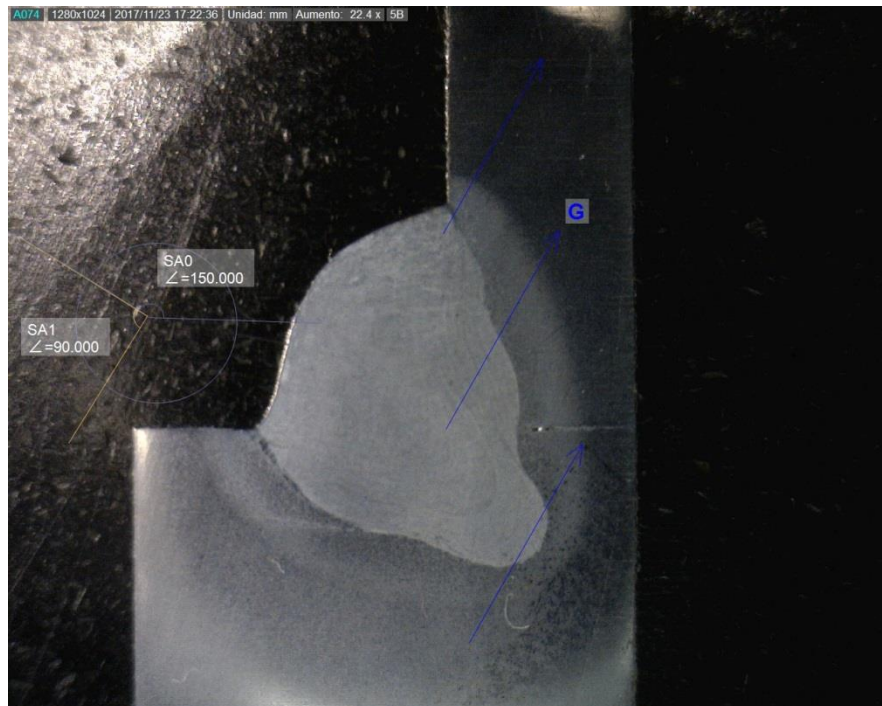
11 Perfil obtenido en cupón de soldadura 6A.
